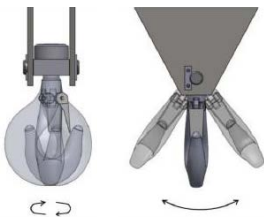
GIROS DO GANCHO SENDO AXIAL (ROLAMENTO) E NO PLANO (EIXO DA TRAVESSA)
